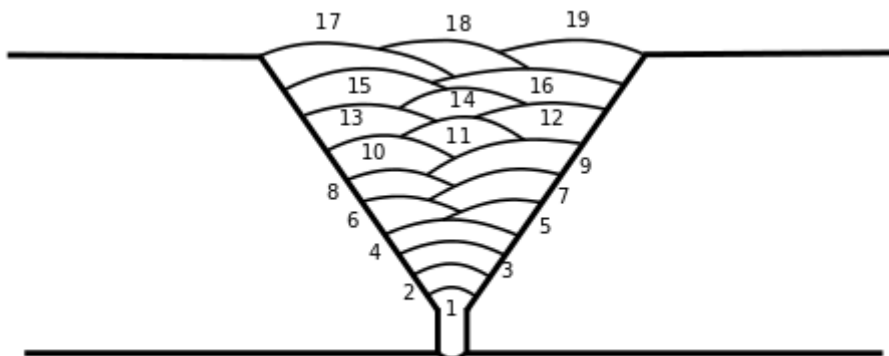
Corpo de prova 3 com restrição – Diagrama dos passe de soldagem GTAW
